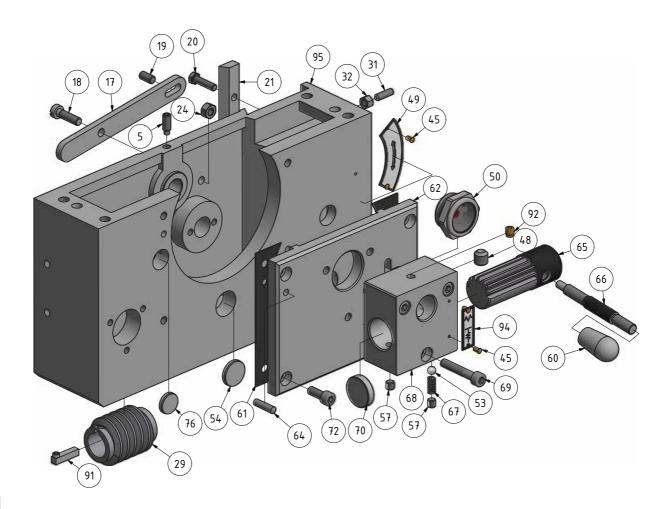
Schlosskasten 1-3 - Apron 1-3
